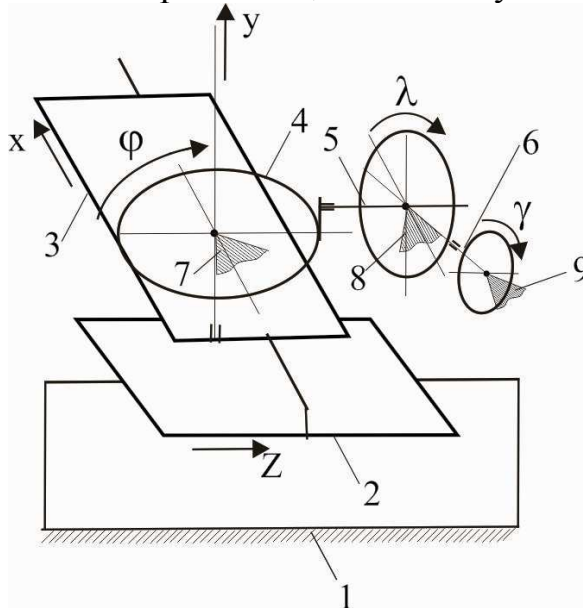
Кинематическая структура токарного станка с мехатронной системой управления тремя кинематическими основными углами лезвия инструментальной системы
